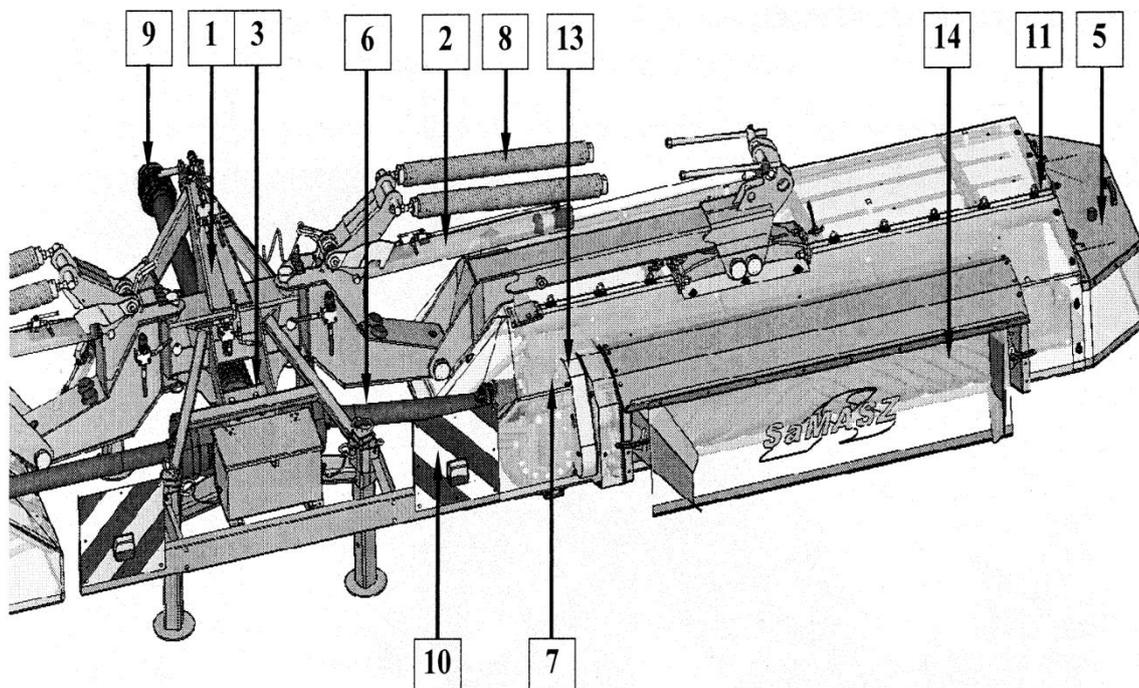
Общий вид двусторонней дисковой косилки с плющилками
